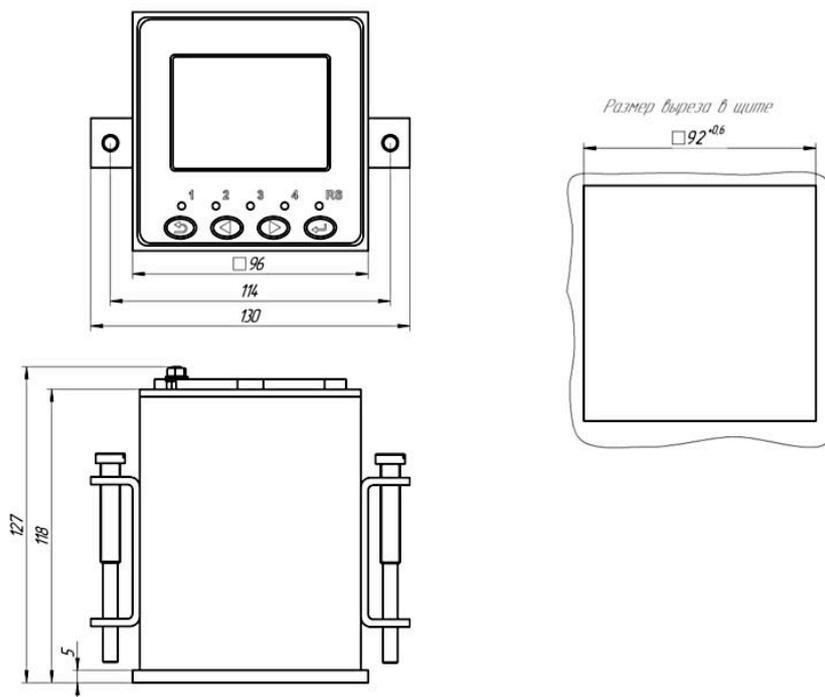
Габаритные размеры измерительного прибора рН-4110 для щитового монтажа
